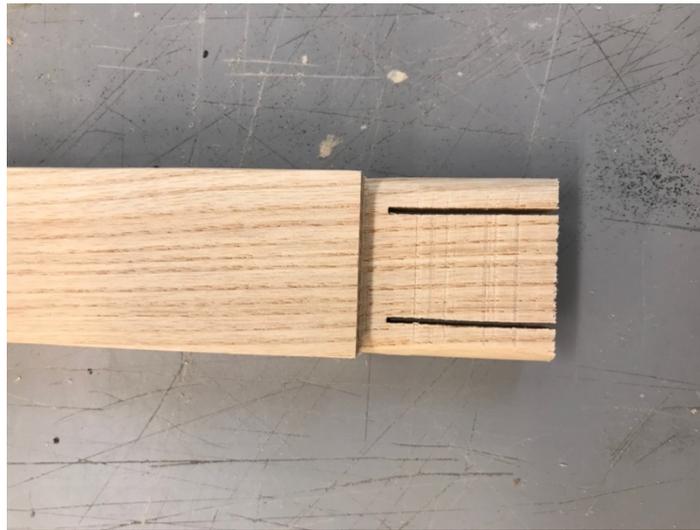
Détail d'assemblage du tenon : Chaise finale
